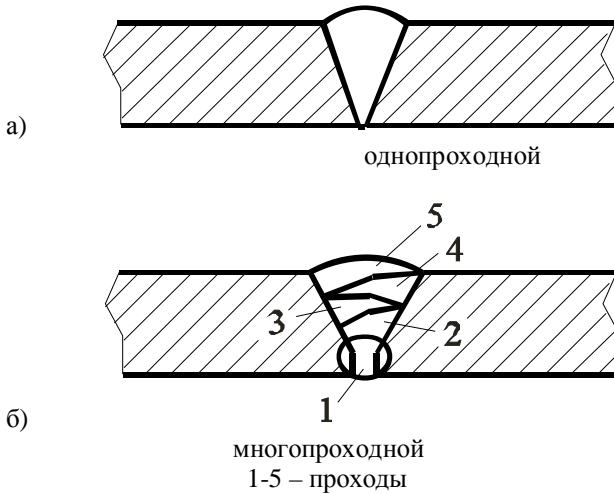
Виды сварных швов по технологии нанесения
